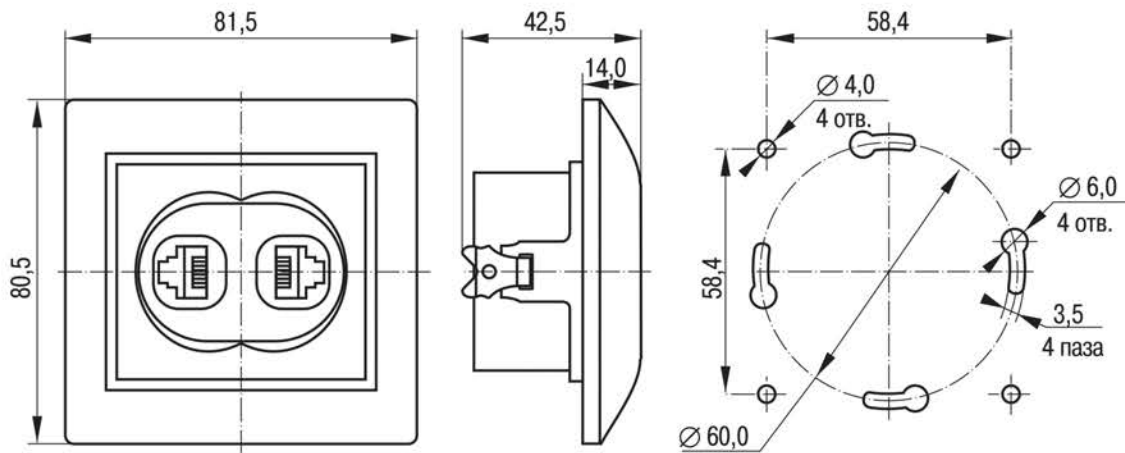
Габаритные и присоединительные размеры РТ12-КБ, РТ12-ККм, РК/Т12-КБ, РК/Т12-ККм
